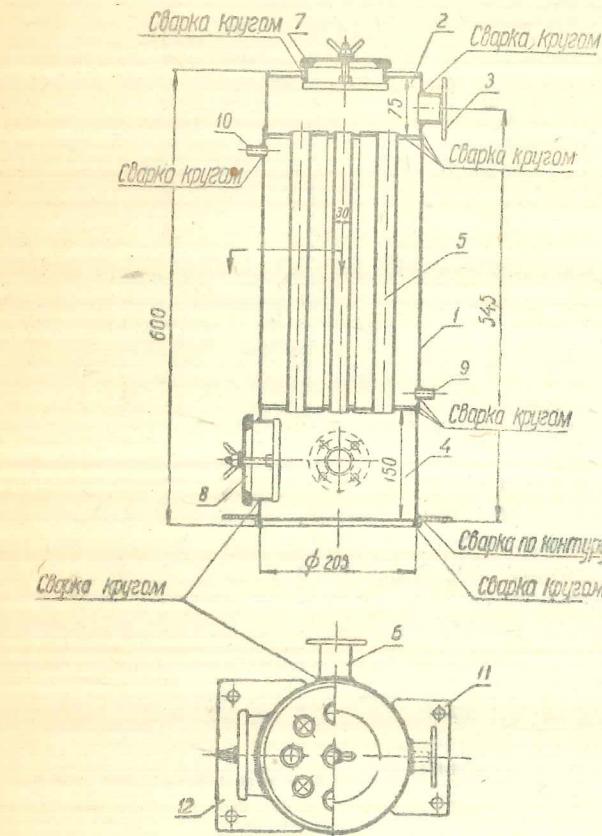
Батарейно-трубчатый охладитель конструкции НИКФИ
